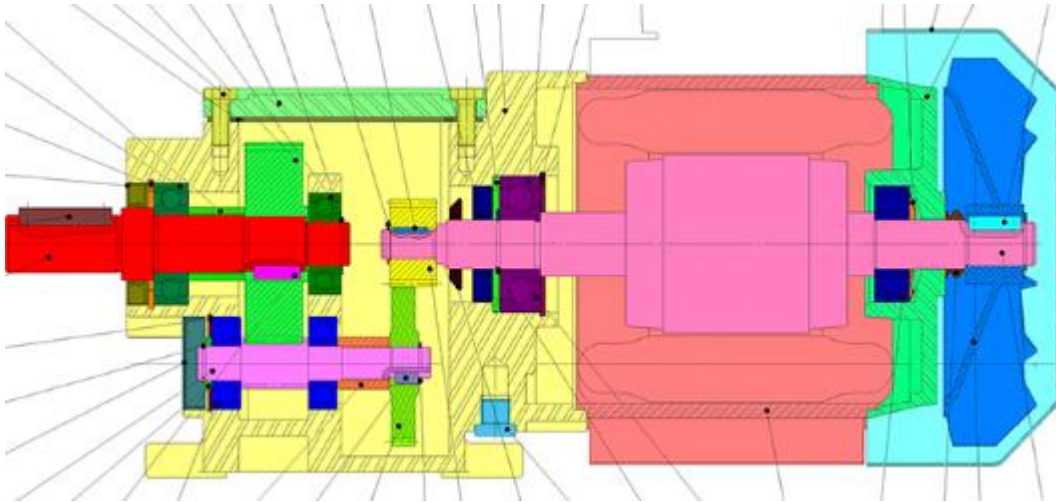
Exemple d'un motoréducteur à train d'engrenages
